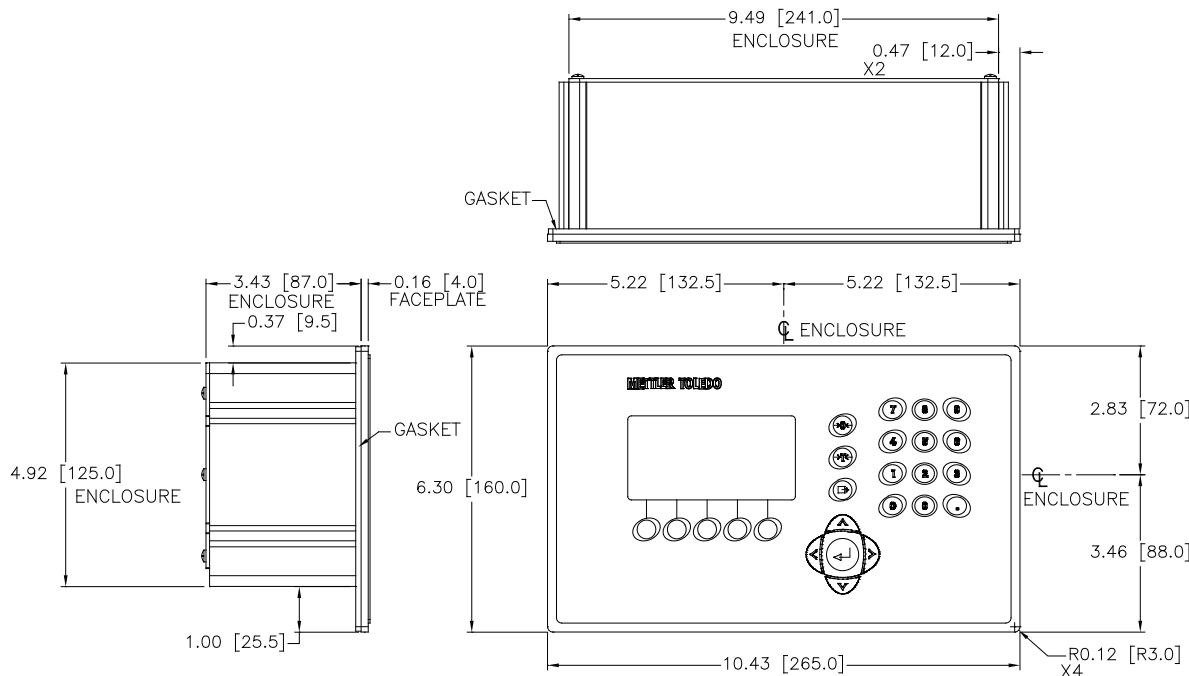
Dimensões do gabinete do IND560 para montagem em painel
